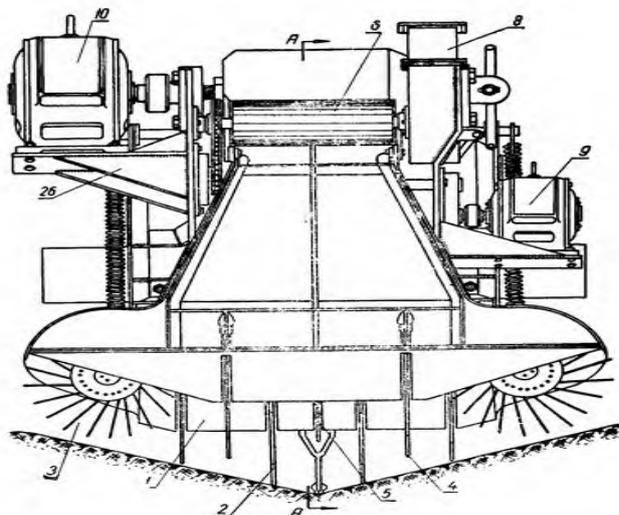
барабан; 2-лучи; 3-щётки; 4-диски; 6-валик; 7-фрезерный барабан; 9, 10-электродвигатель; 25-диск щупа; 29-рукоятка; 30-трос; 33-магнитный пускатель; 34- пускатель; 36-лапки; 37-полости.
